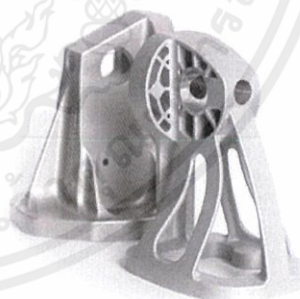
ระบบผงยิปซัม+สี Ink Jet (Powder 3D Printer หรือ ColorJet Printing)
